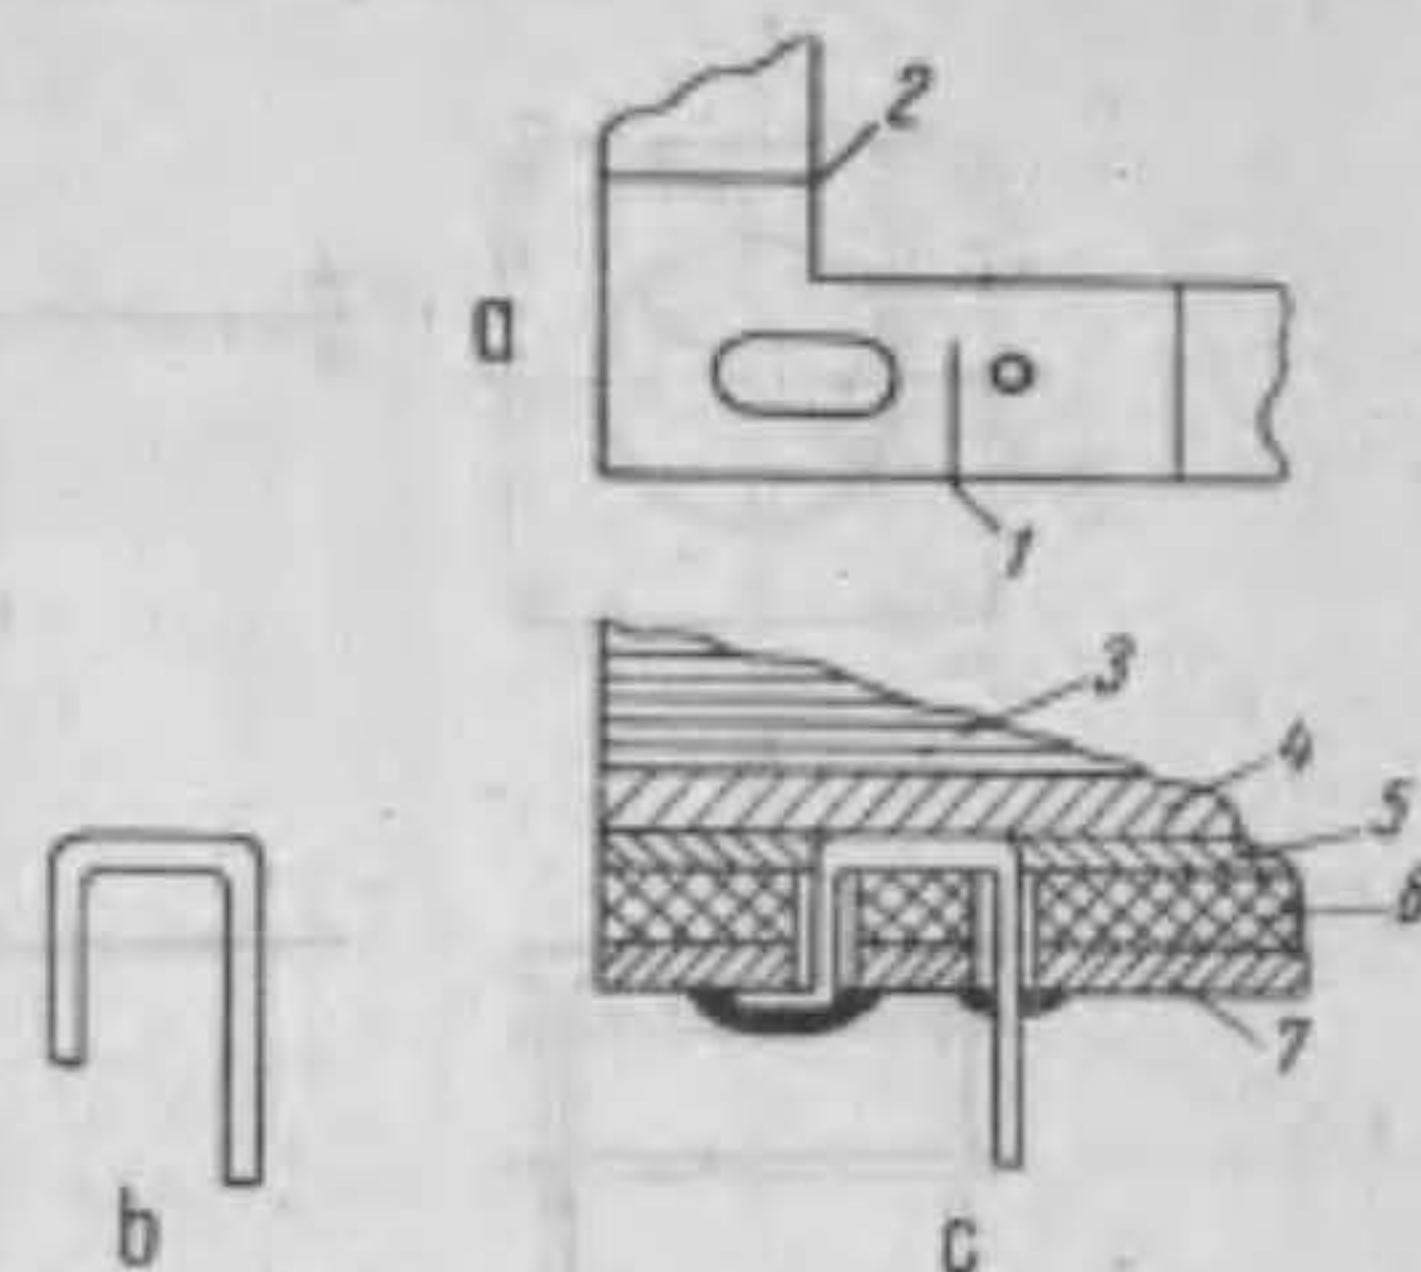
Transformator armat pentru fixarea pe placa imprimată: a - suprafața de lipire a conexiunilor transformatorului; b - conexiune de fixare înainte de lipire; c - transformator montat pe placă; 1 - linie de separație termică; 2 - linie de separație electrică; 3 - miezul transformatorului; 4 - strat izolator din hîrtie; 5 - adeziv; 6 - placă de pertinax; 7 - foită de Cu.
